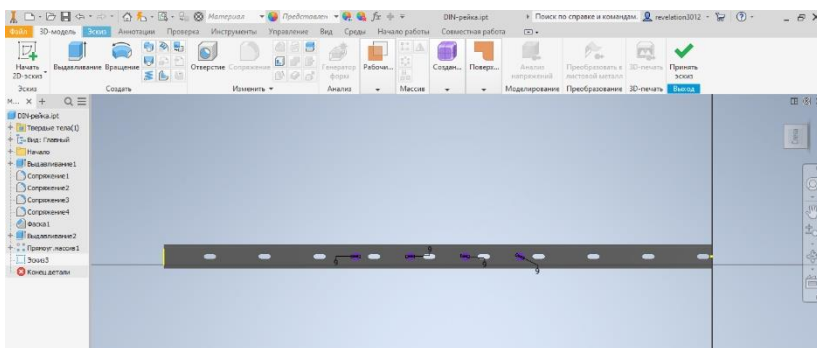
Ескіз створення отворів для болтового з'єднання DIN-рейки
